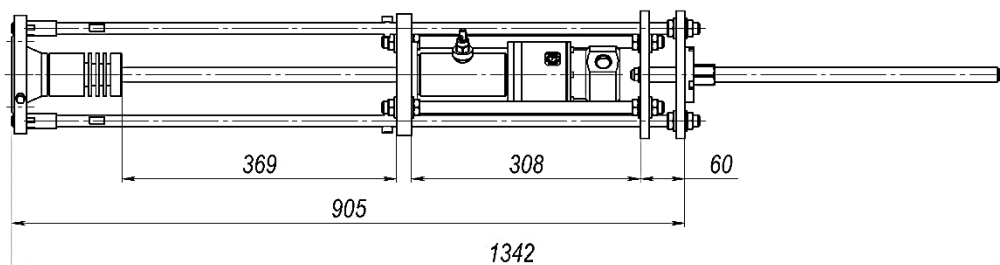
Габаритные размеры приемопередатчика КТМ100 М ЛБ (с установочным приспособлением)
